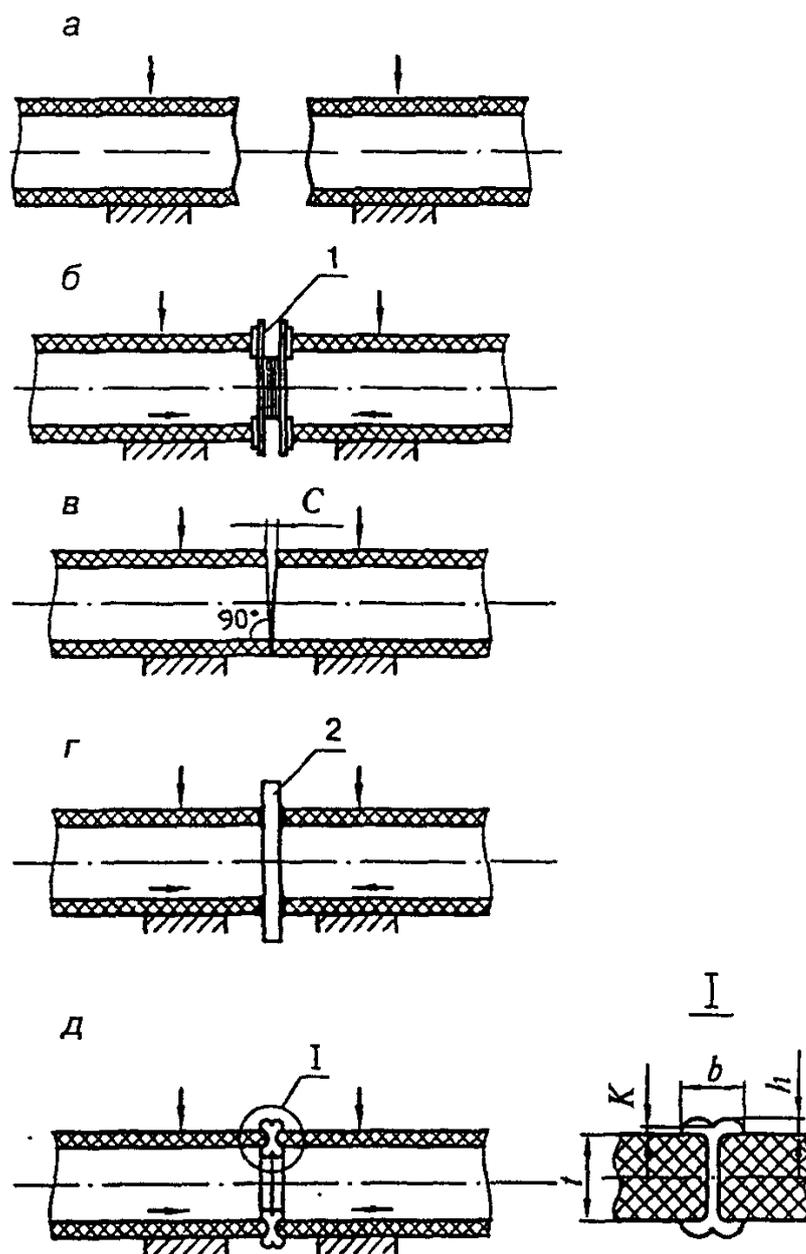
Последовательность процесса сборки и сварки встык труб из полиэтилена [12]
